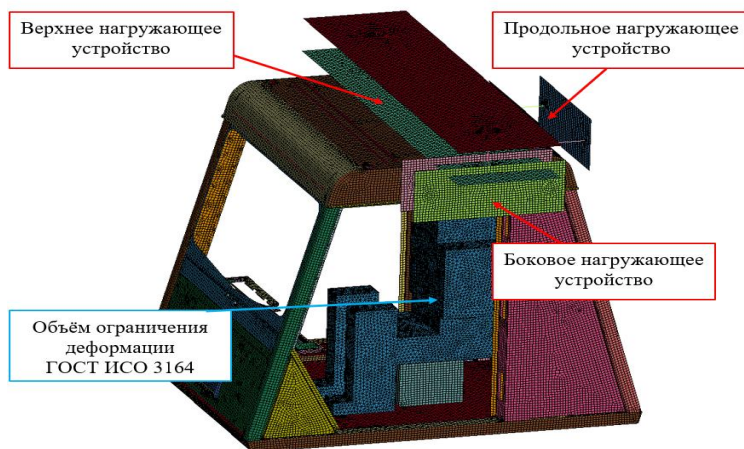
Конечно-элементная модель кабины карьерного самосвала с нагружающими устройствами
